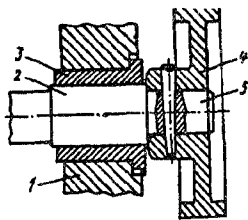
Сборочная единица с основными и вспомогательными сборочными базами
